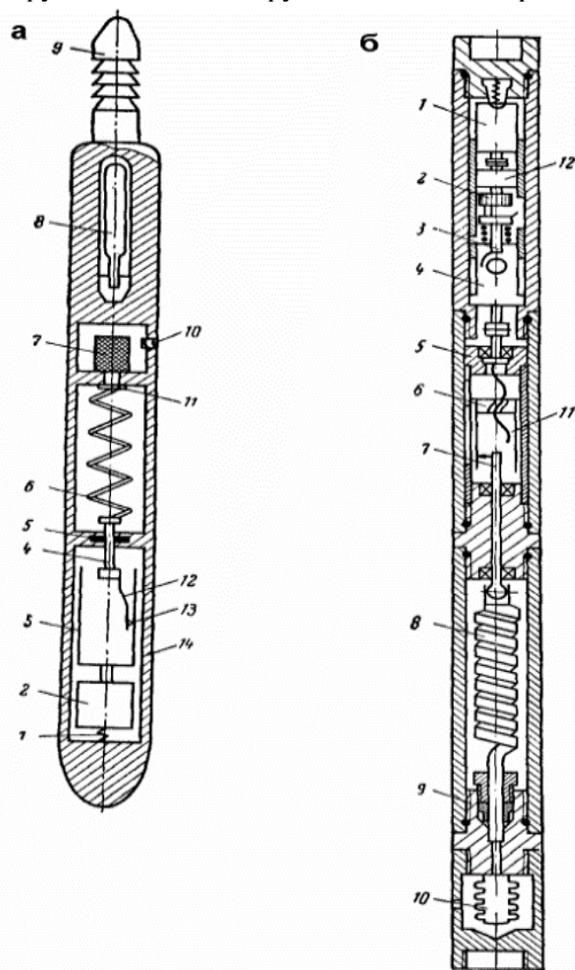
Глубинный манометр: а – поршневой: 1,6 – пружины; 2 – часовой механизм; 3 – барабан; 4 – поршень; 5 – сальниковое уплотнение; 7 – фильтр; 8 – ртутный термометр; 9 – головка; 10 – канал; 11 – якорь; 12 – держатель; 13 – игла; 14 – корпус прибора; б – с трубчатой многовитковой пружиной: 1 – часовой привод механизма задержки; 2 – лимб установки времени задержки; 3 – стопор баланса часов; 4 – часовой механизм записи; 5 – каретка; 6 – барабан с диаграммным бланком; 7 – игла; 8 – пружина; 9 – узел уплотнения; 10 – сильфонный разделитель; 11 – винт; 12 – редуктор.
